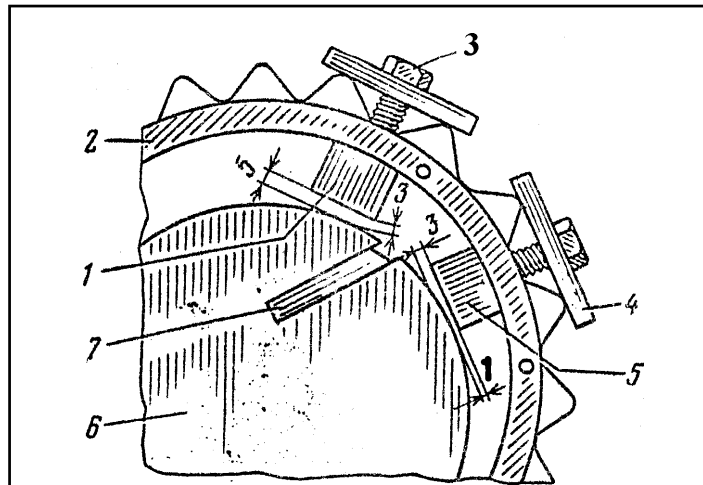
Схема сопряжения режущих частей крупорушки: 1 - вкладыш (первый); 2 - статор; 3 - болт крепления вкладыша; 4 - шайба (плашка) болта крепления вкладыша; 5 - вкладыш (второй); 6 - ротор; 7 - стальная пластина (вставлена в паз ротора)
